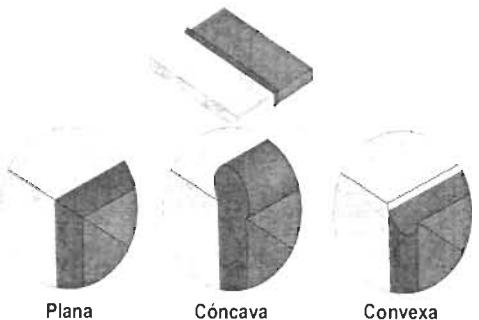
Forma de la superficie del Cordón de soldadura.
